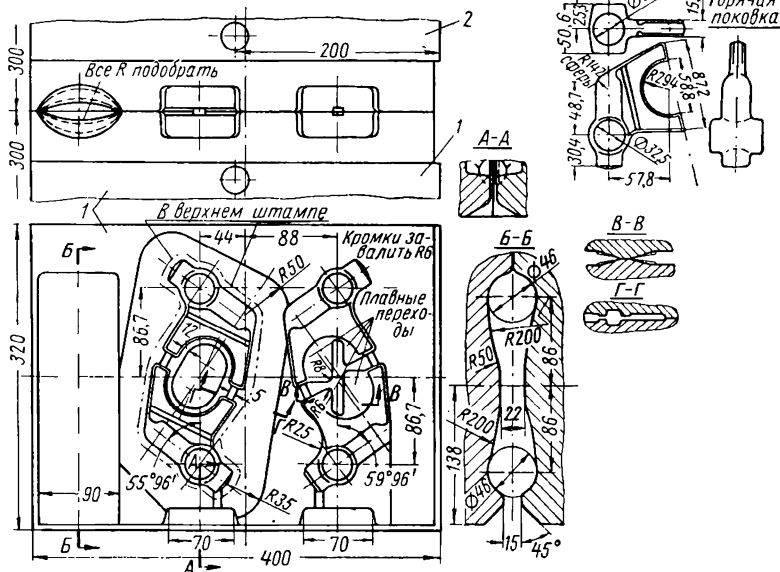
Молотовый штамп для поковки вилки включения блокировки дифференциала
